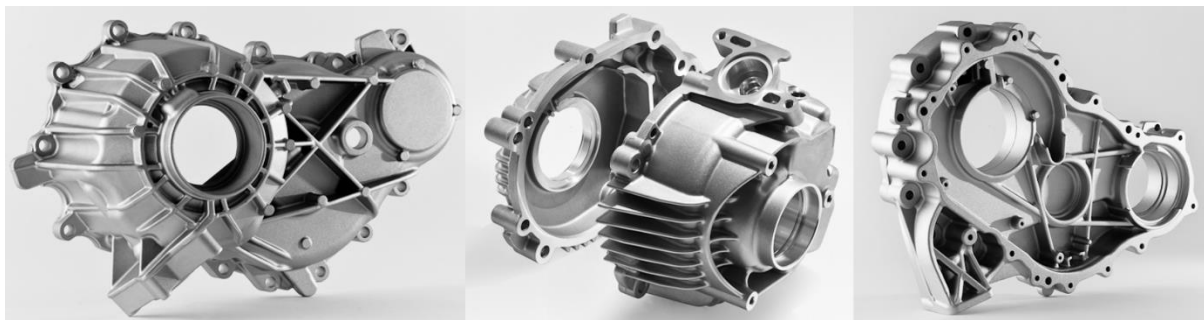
Componentes fundidos e maquinados pela SLM [4].
